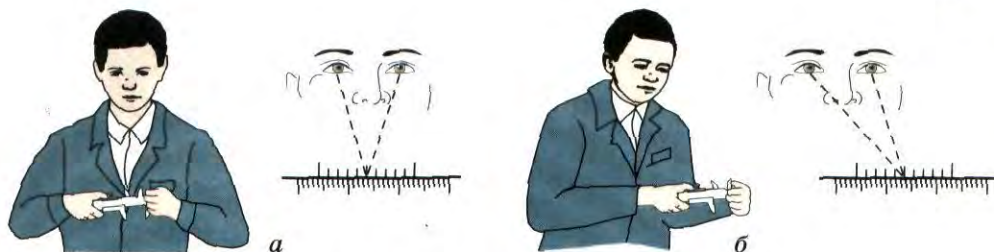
Вимірювання і контроль розмірів деталей штангенциркулем ШЦ-I:
